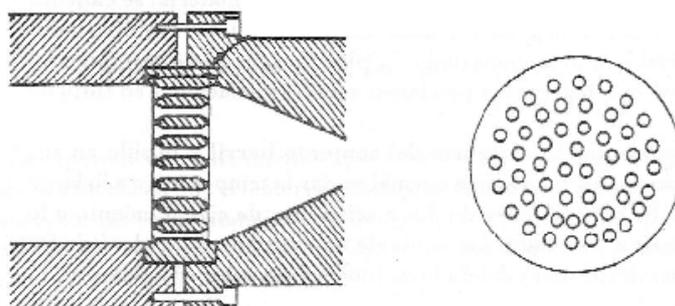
Plato rompedor del cilindro de la extrusora.
